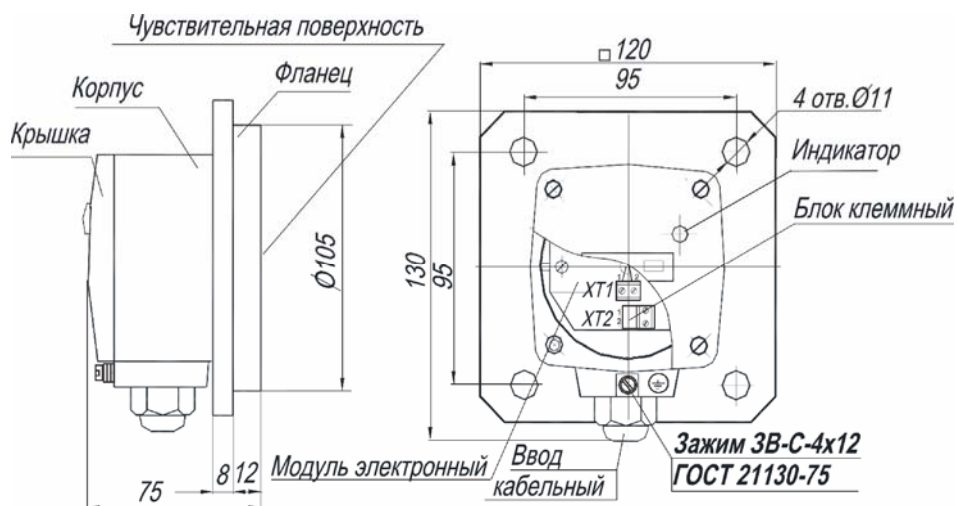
Внешний вид и габаритные размеры датчика
